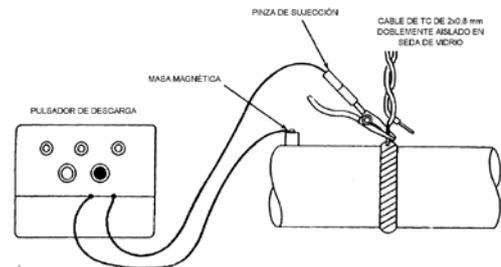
Equipo de Soldadura Capacitiva.
